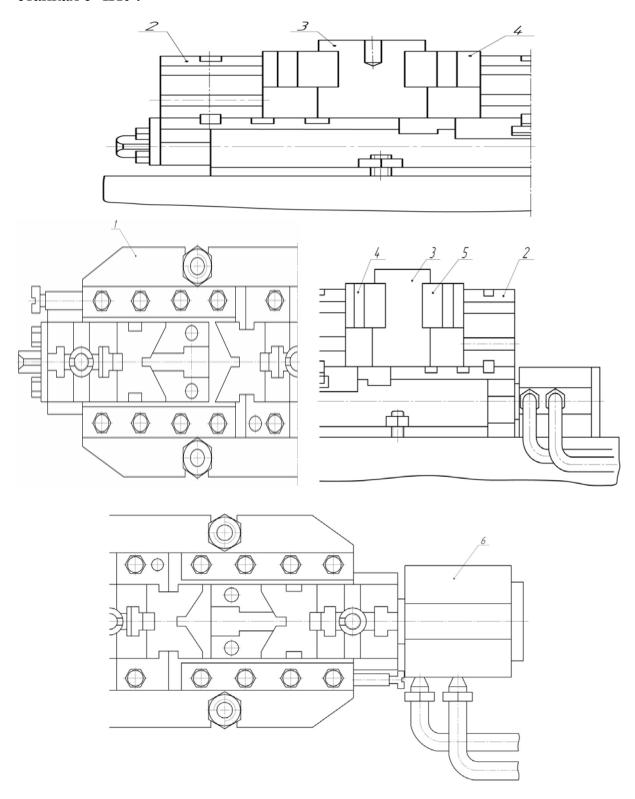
Двухместное приспособление для установки валика: 1 — плавающий зажим; 2 — опора; 3 — заготовка; 4 — неподвижная призма; 5 — подвижная призма; 6 — гидроцилиндр
